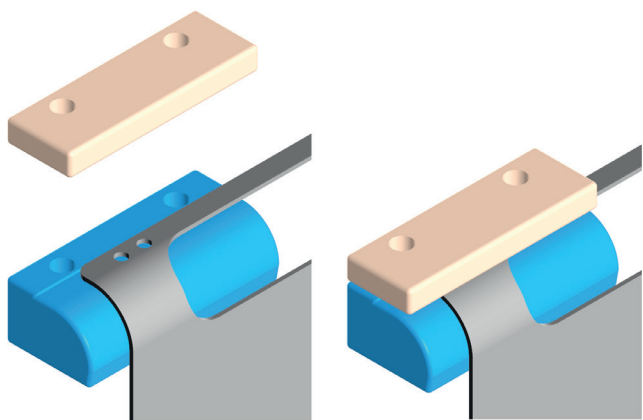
Процесс штамповки штампами из PLA-пластика с помощью винтовых струбцин и готовой детали
